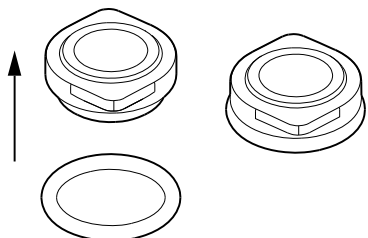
Монтаж уплотнительного кольца на неподвижной части торцевого уплотнения
